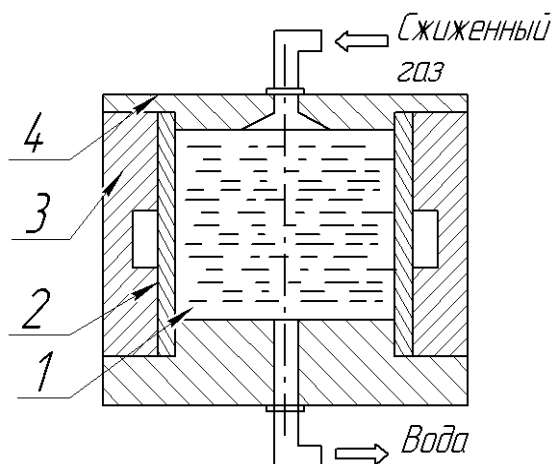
Впрыск порции сжатого газа над формообразующей полостью оснастки: 1 – среда передающая (вода), 2 – заготовка кольцевая, 3 – матрица, 4 – крышка матрицы
